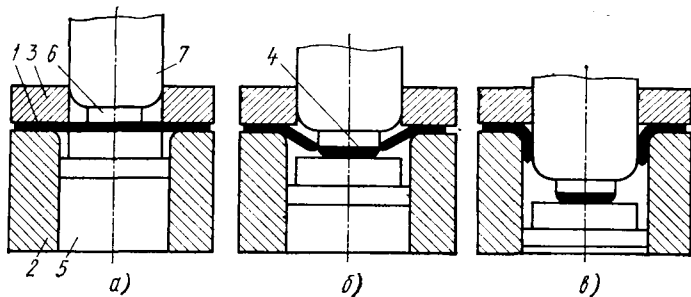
Схема совмещенного способа пробивки и отбортовки отверстия в горловине корпуса бензобака
